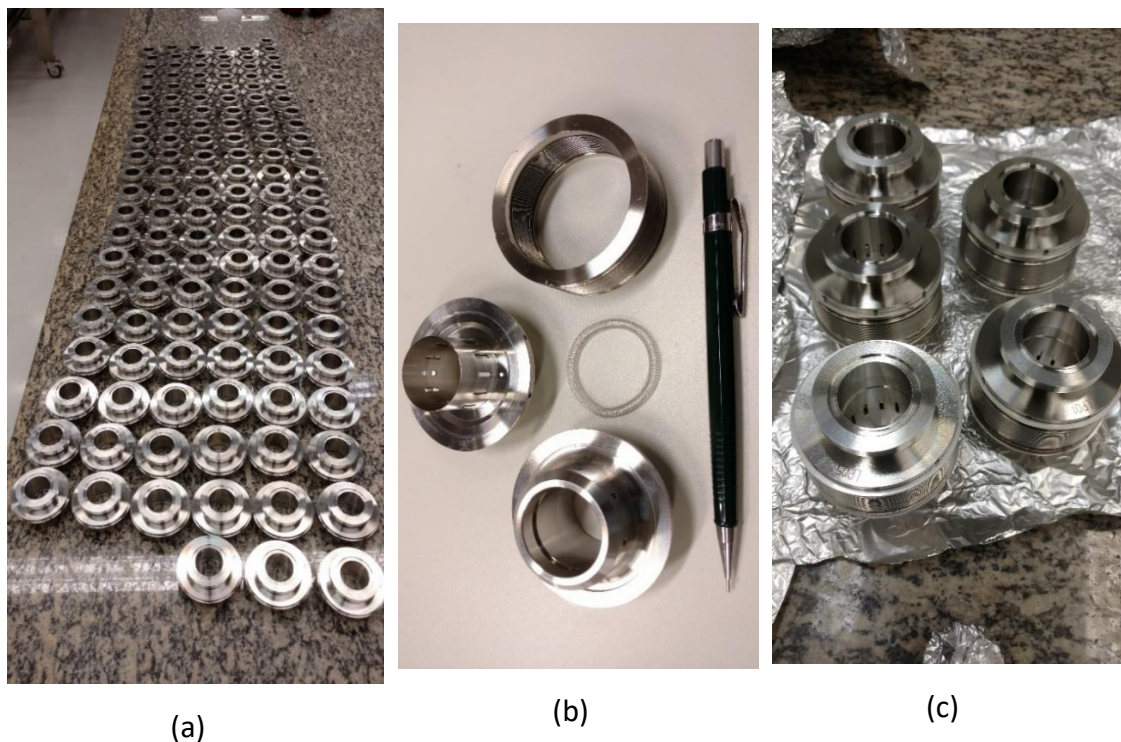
(a) Parte das peças “fêmea” para a montagem dos 400 bellows modelo “telescópico”, (b) componentes para a montagem e soldagem de um conjunto bellows; e (c) conjuntos bellows prontos já montados e soldados.
